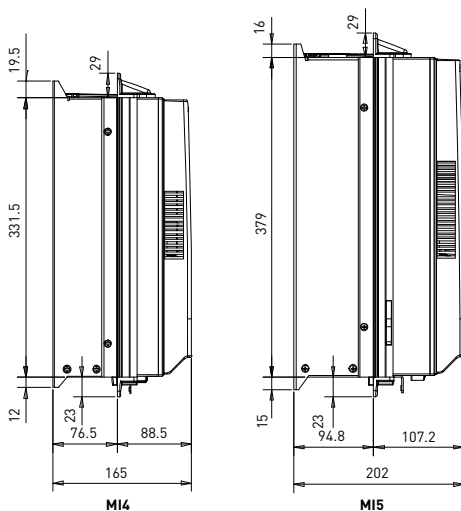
Размеры по глубине для фланцевого крепления приводов типоразмеров MI4 и MI5 (единица: мм)
